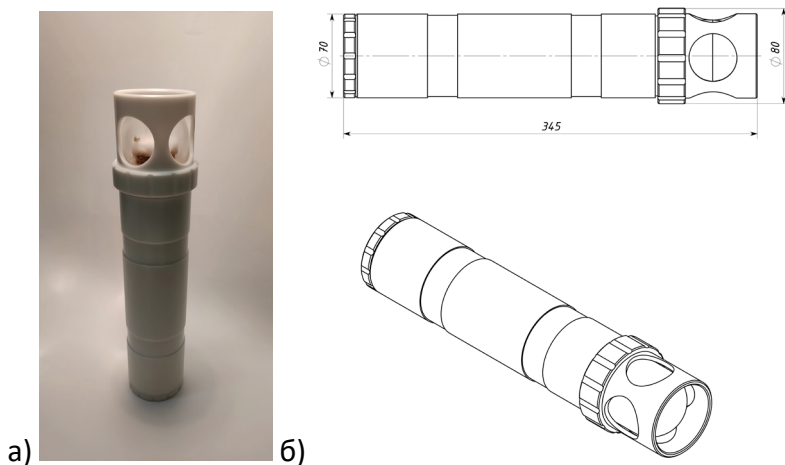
а) внешний вид поискового маяка в сборе, б) чертеж корпуса
